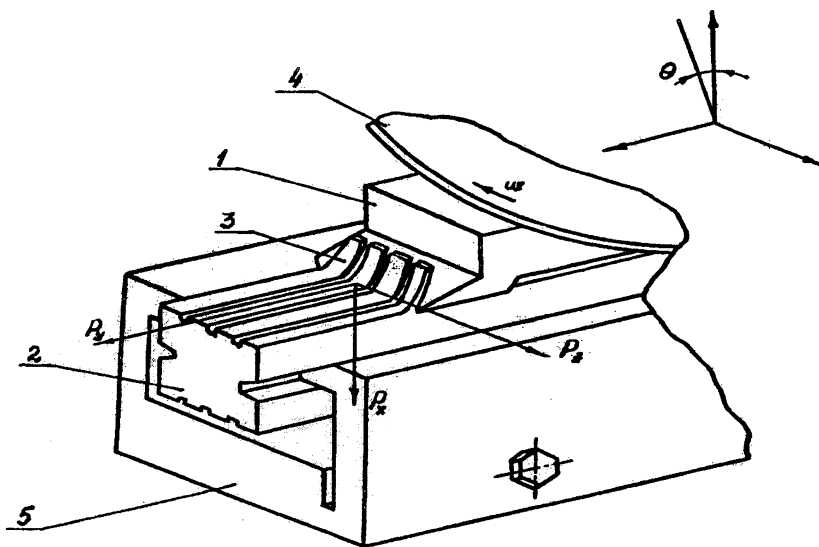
Схема оребрения плоских труб: 1 – резец; 2 – заготовка; 3 – ребро; 4 – планшайба; 5 - приспособление
